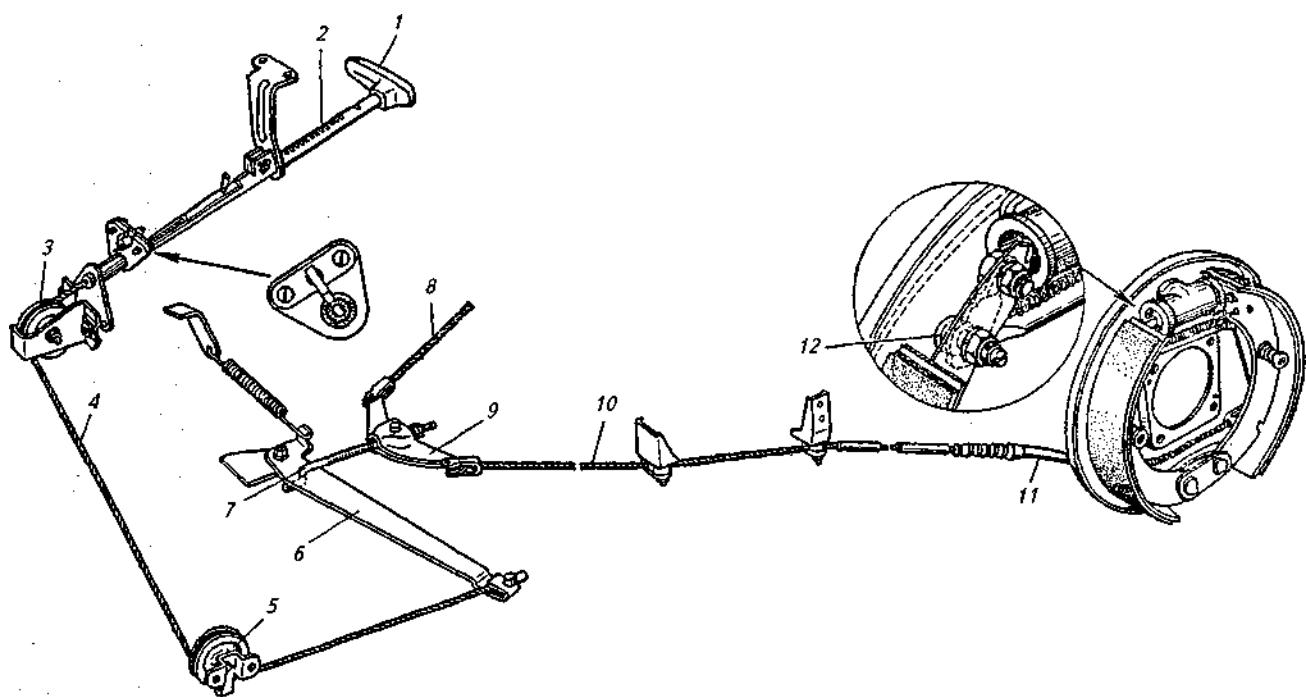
Стояночный тормоз, действующий на задние колеса: 1 – рукоятка; 2 – рычаг; 3,5 – ролики троса; 4 – передний трос; 6 – промежуточный рычаг; 7 – стержень; 8,10 – тросы привода тормозных механизмов; 9 – уравнитель тормоза; 11 – трубка; 12 – эксцентриковая ось разжимного рычага
